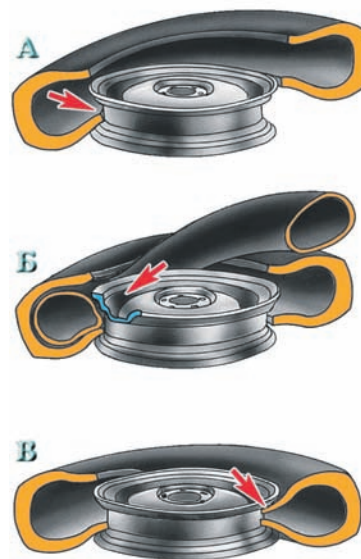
Установка шини на обід: А – установка внутрішнього борту покришки; Б – заправка камери в покришку; В – установка зовнішнього борту покришки
